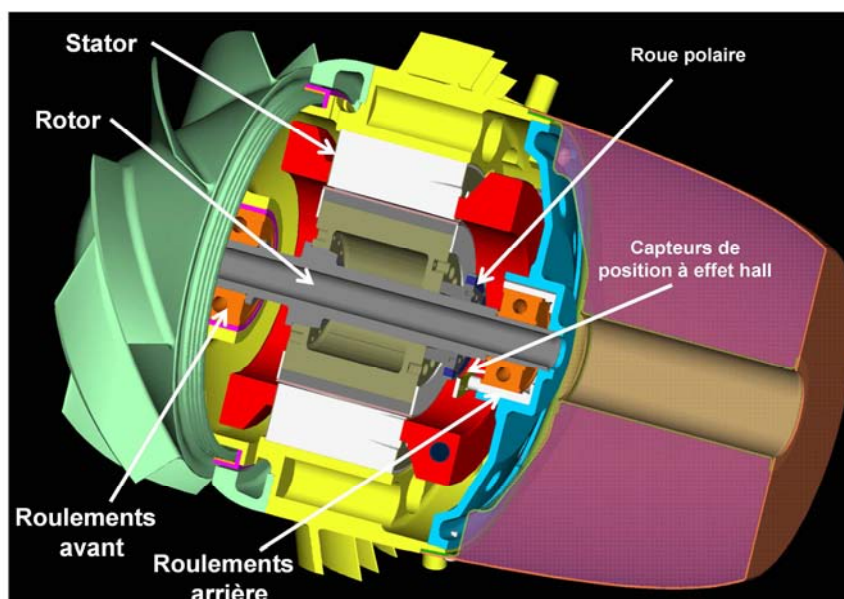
Vue de coupe d'un ensemble moteur avec la roue du ventilateur - (origine TECHNOFAN)
